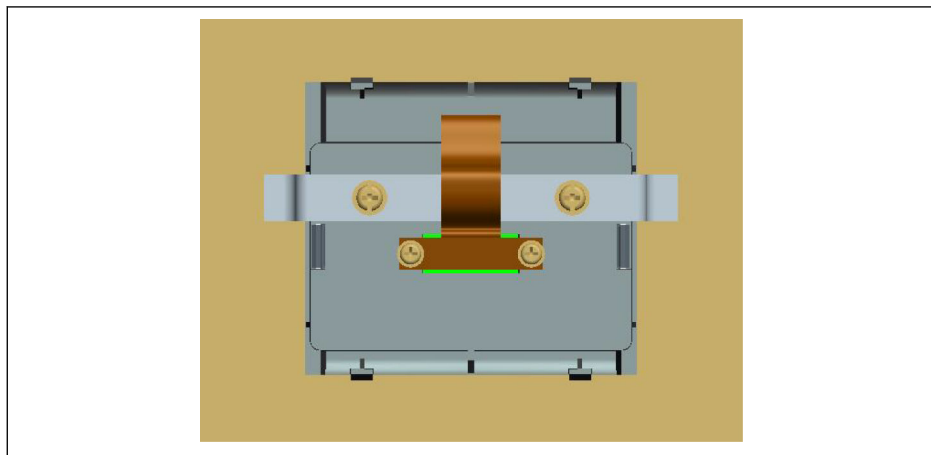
Raccorder et fixer le câble (vue arrière)
